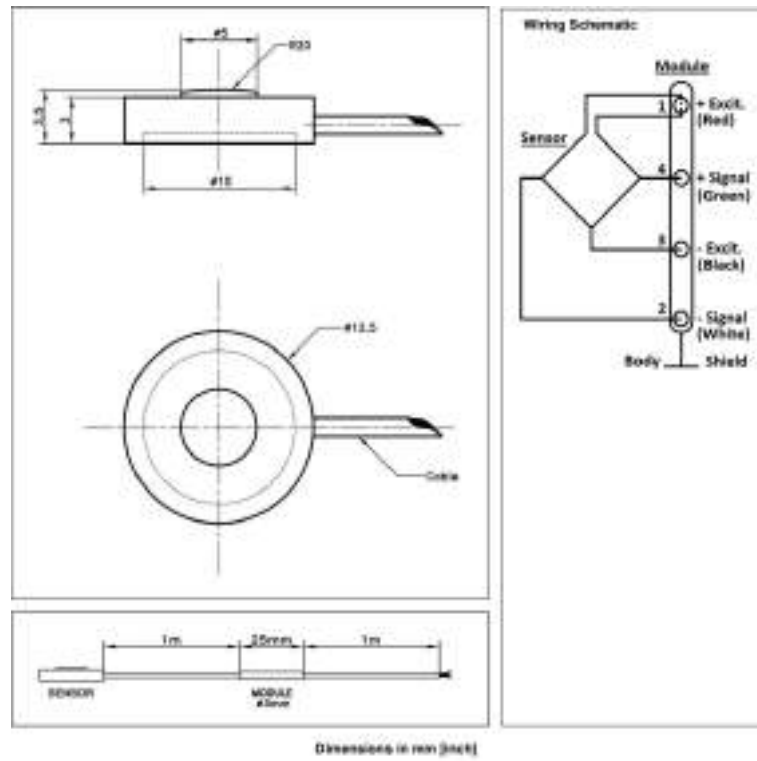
Dimensiones del sensor de presión de contacto XFL212R. Fuente: [29]
